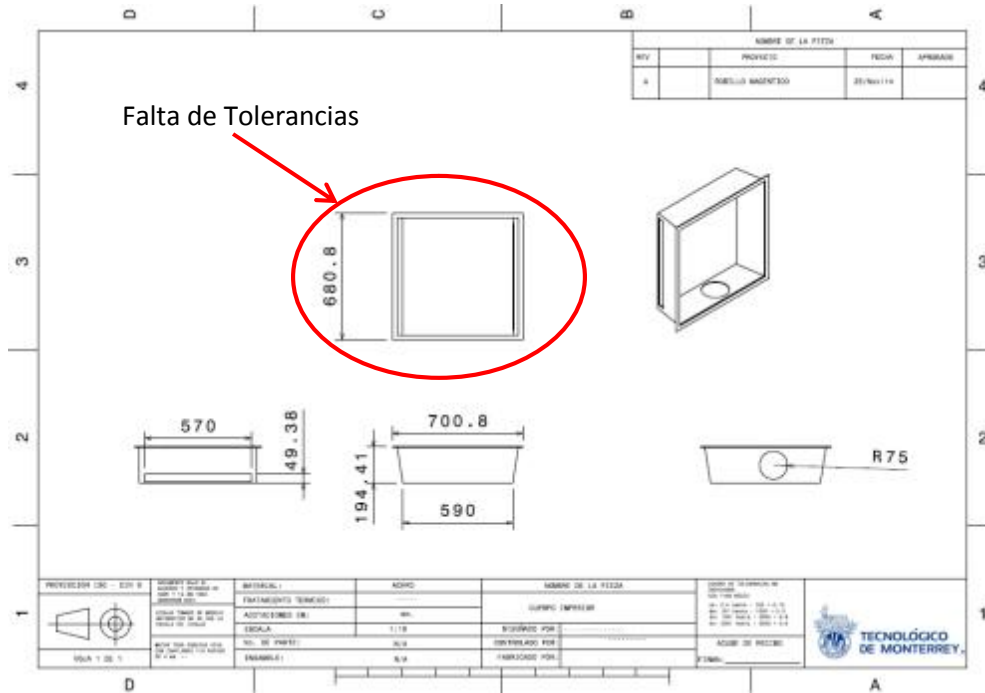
Plano con falta de tolerancias y normas
